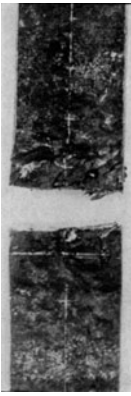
Querschnitt durch schlechte autogene Schweißung, Schlackenschichten, insbesondere am links gelegenen Rande, die wie Anbrüche wirken. Der Kessel, aus dem das Stück stammt, explodierte.
